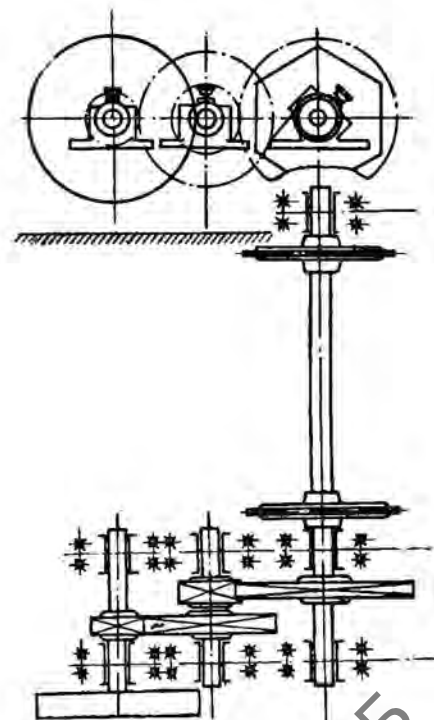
Схема привода для цепей с одной зубчатой передачей Шахтостроля.
